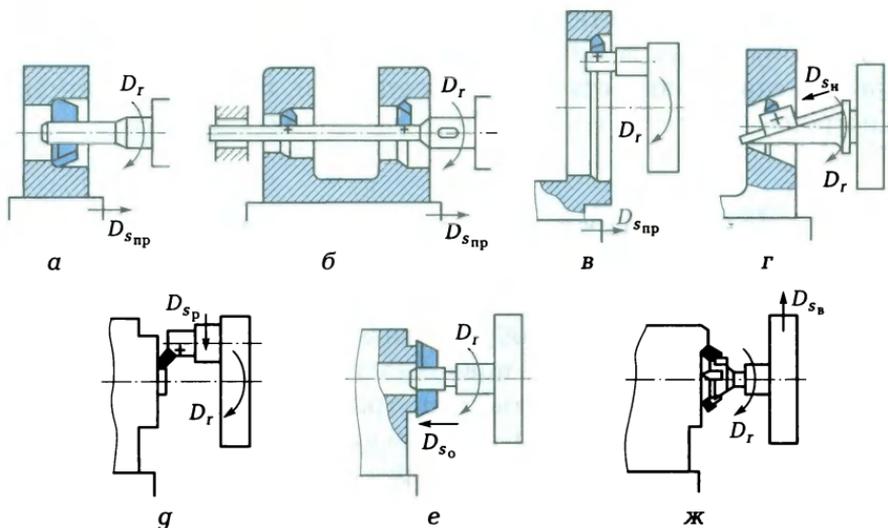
Схемы обработки заготовок на горизонтально-расточных станках: а, б, в, г — растачивание; г, е — подрезание торцов резцами; ж — фрезерование
